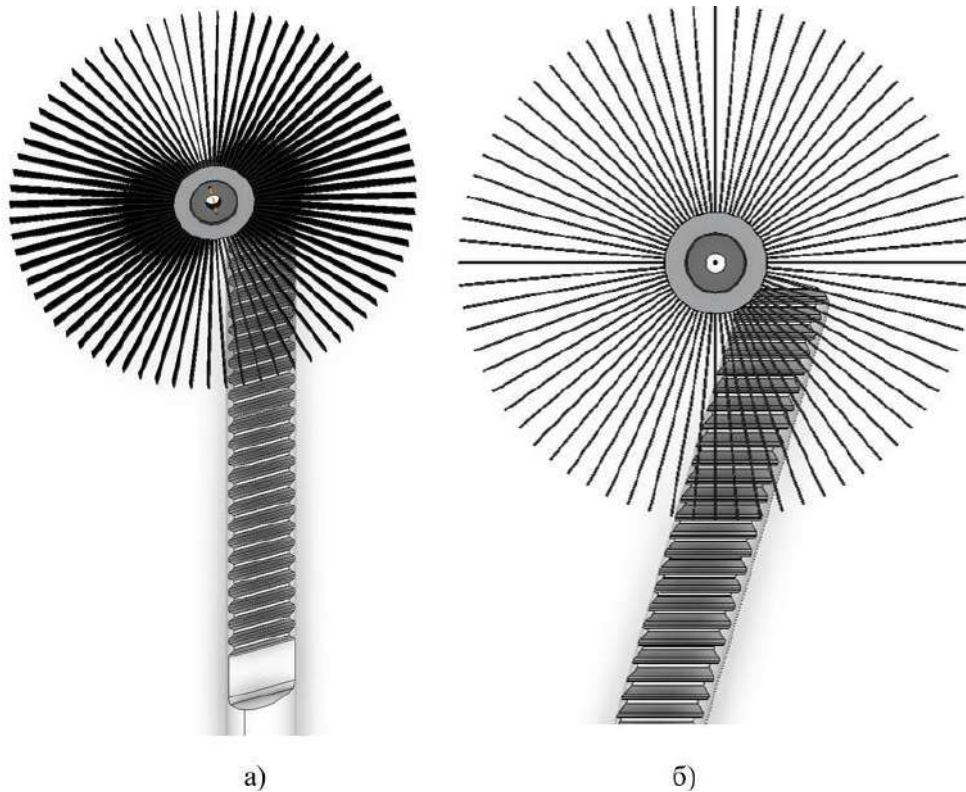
Обробка рульової рейки гнучким інструментом: а – вид зверху; б – вид нормаллю до інструменту
